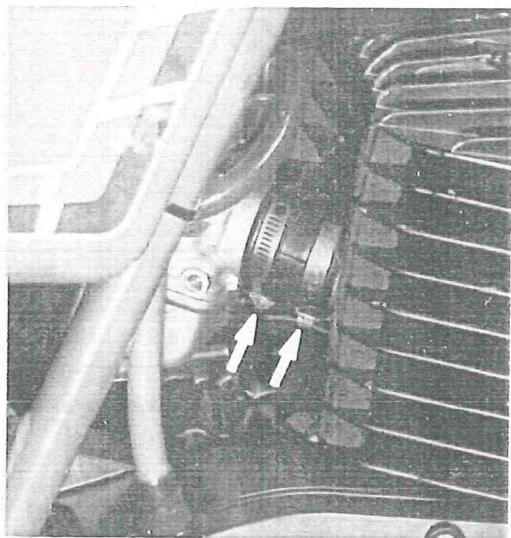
Fascette fissaggio manicotto cilindro-carburatore
